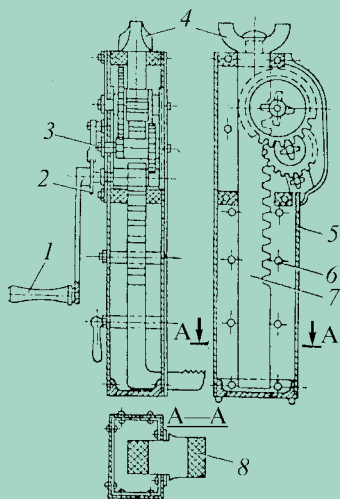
Схема реечного домкрата с безопасной рукояткой: 1 — рукоятка; 2 — храповое колесо; 3 — собачка, удерживающая колесо и укрепленная на станине; 4 — опорная подушка; 5 — металлическая станина; 6 — болты, скрепляющие станину с распорными втулками; 7 — зубчатая рейка, перемещающаяся внутри станины по направляющим; 8 — опорная лапа с насечкой
